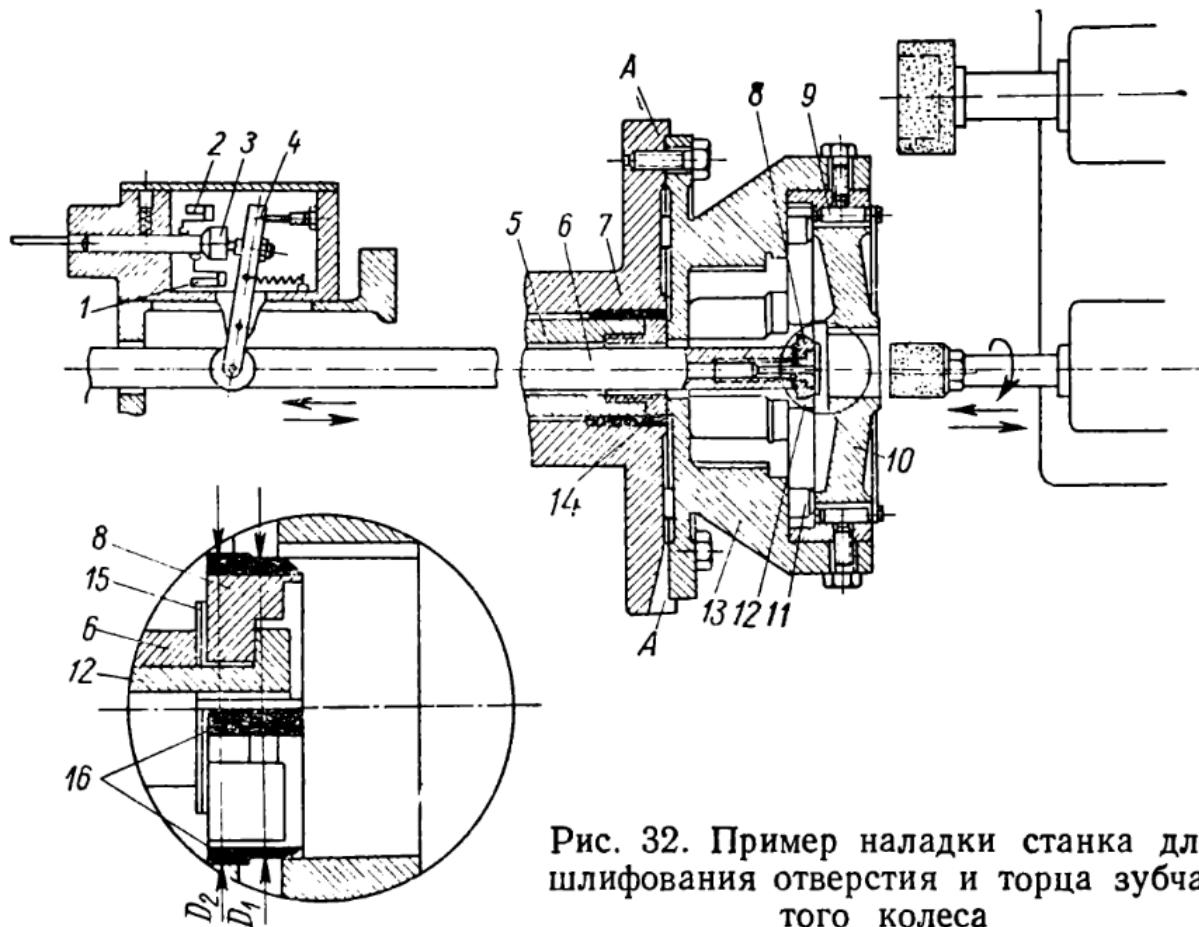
Пример наладки станка для шлифования отверстия и торца зубчатого колеса
